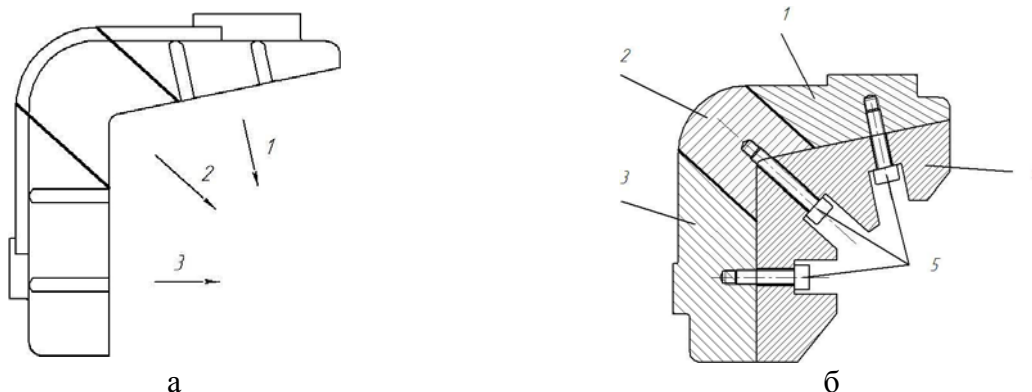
Схема разъединения готового изделия от формообразующих деталей (а) и стенд для сборки формы (б):
